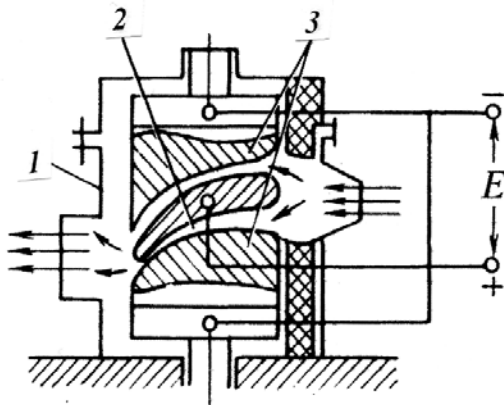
Схема електрохімічної обробки пера лопатки ГТД
